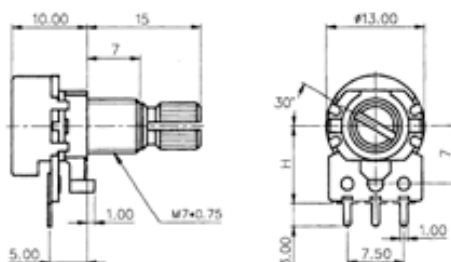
Габаритні розміри змінного резистора 16K1
